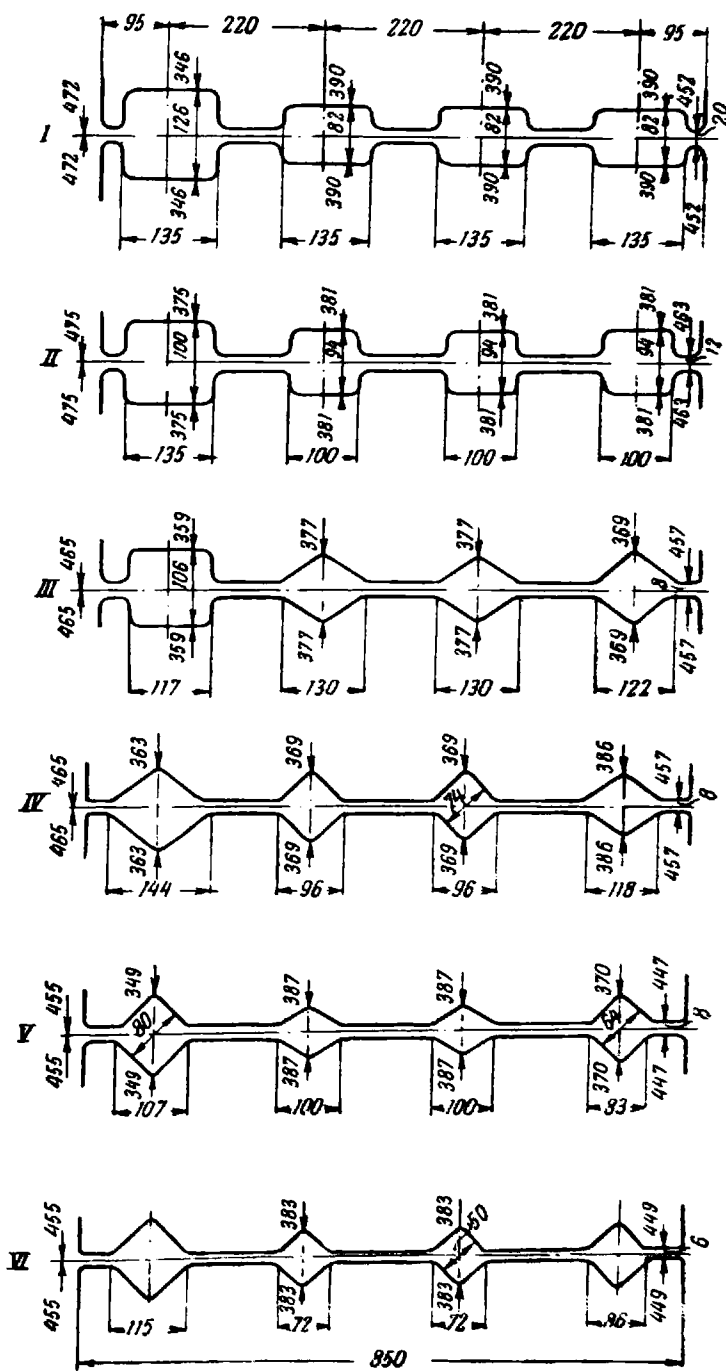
Калибровка валков второй группы клетей непрерывного заготовочного стана 800/630/450
